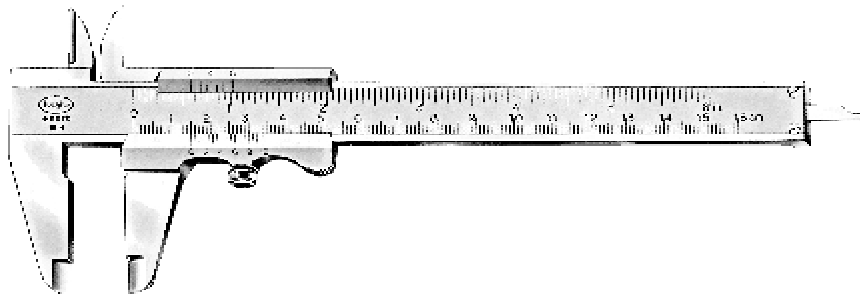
Общий вид штангенциркулей с отсчетом по нониусу MarCal 16 N
